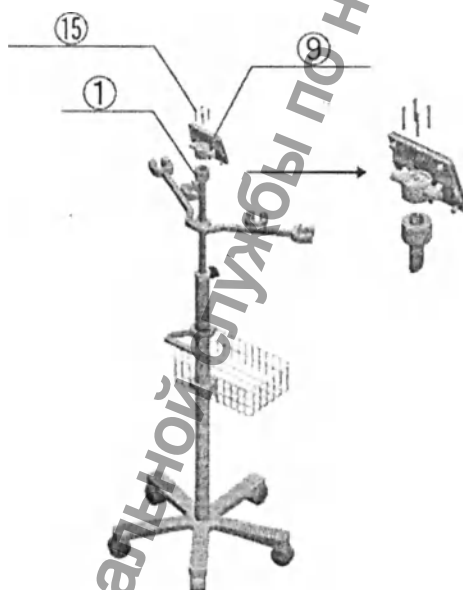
Сборка медицинской стойки Endostand Шаг 6
